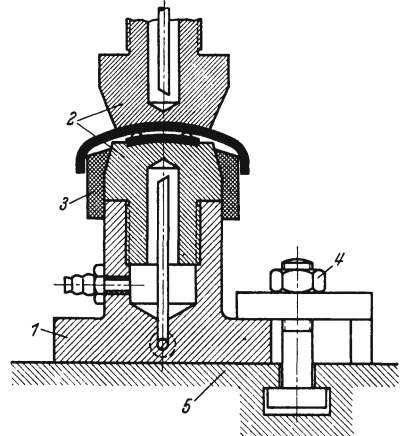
Buckelschweißwerkzeug mit Flächen-elektroden für kleines Werkstück.
